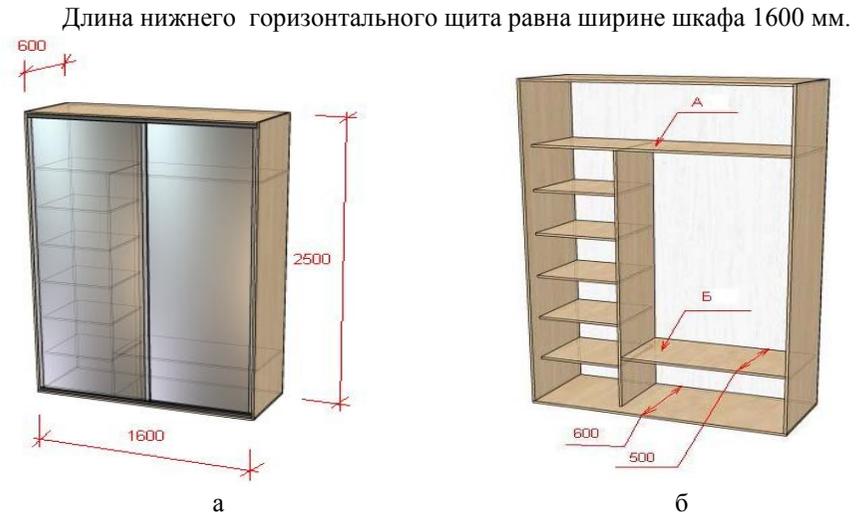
Шкаф-купе: а – общий вид; б – внутренний шкаф
